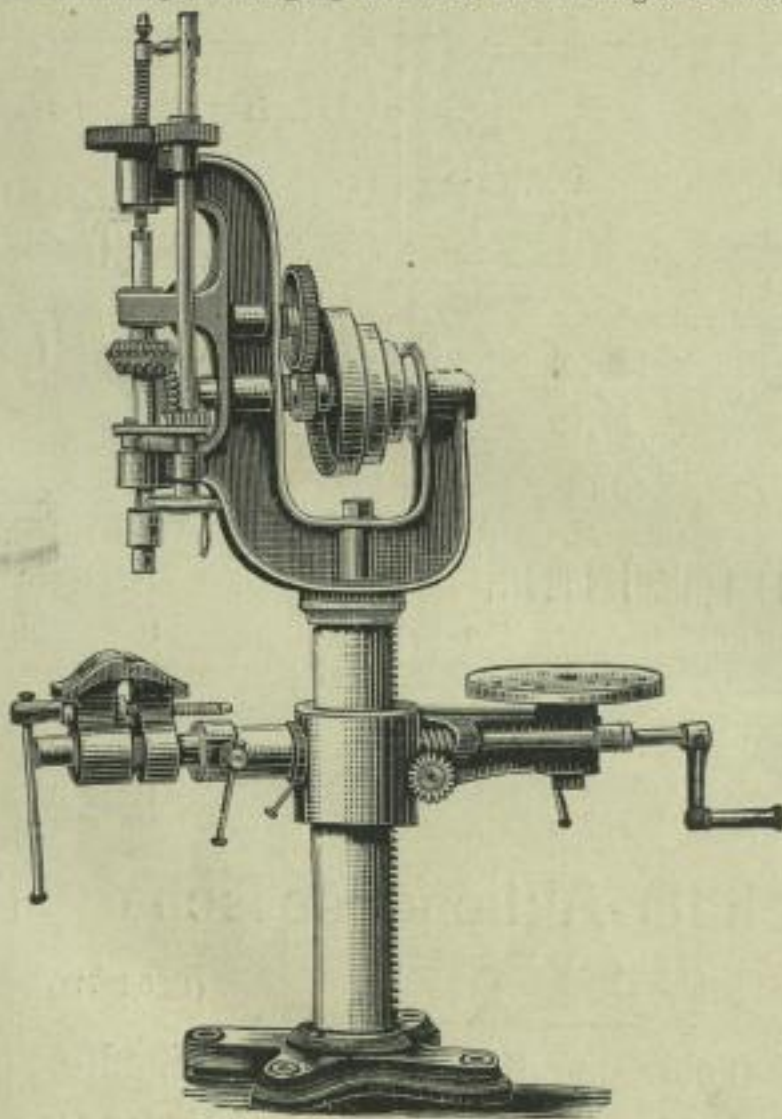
Säulenbohrmaschine für Kraftbetrieb.
